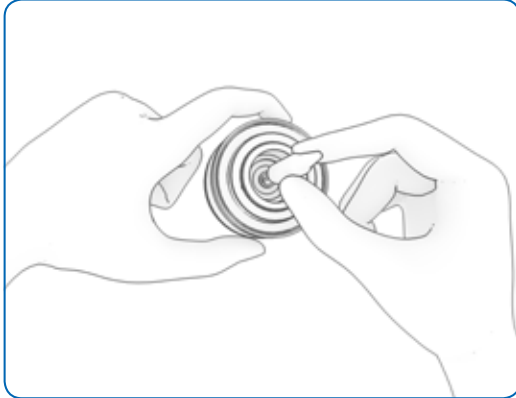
Entfernen des Rückschlagventils mithilfe des Werkzeugs – Teil 1
